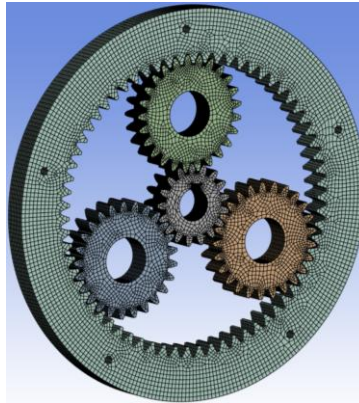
Mallado del tren de engranajes propuesto en ANSYS.
